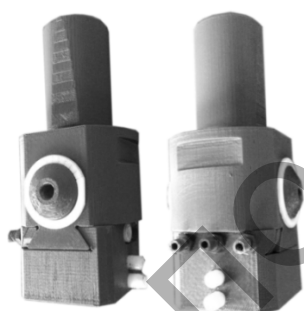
Макет расточного патрона, выполненный с применением технологий трехмерной печати
